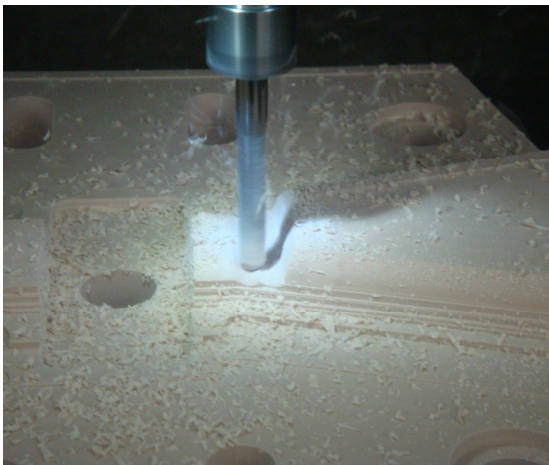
Výroba hornej dosky- operácia cavity mill- 10V
